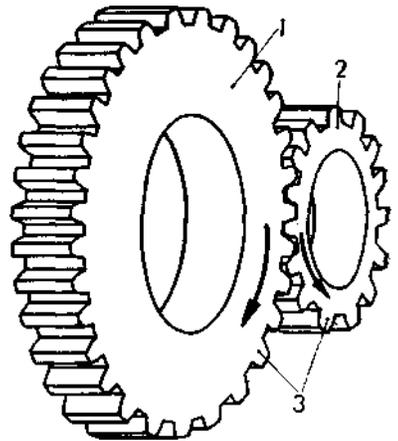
Transmisión del movimiento entre dos engranajes. — 1. Rueda del eje de reducción. — 2. Piñón del eje principal. — 3. Dientes del engranaje.
